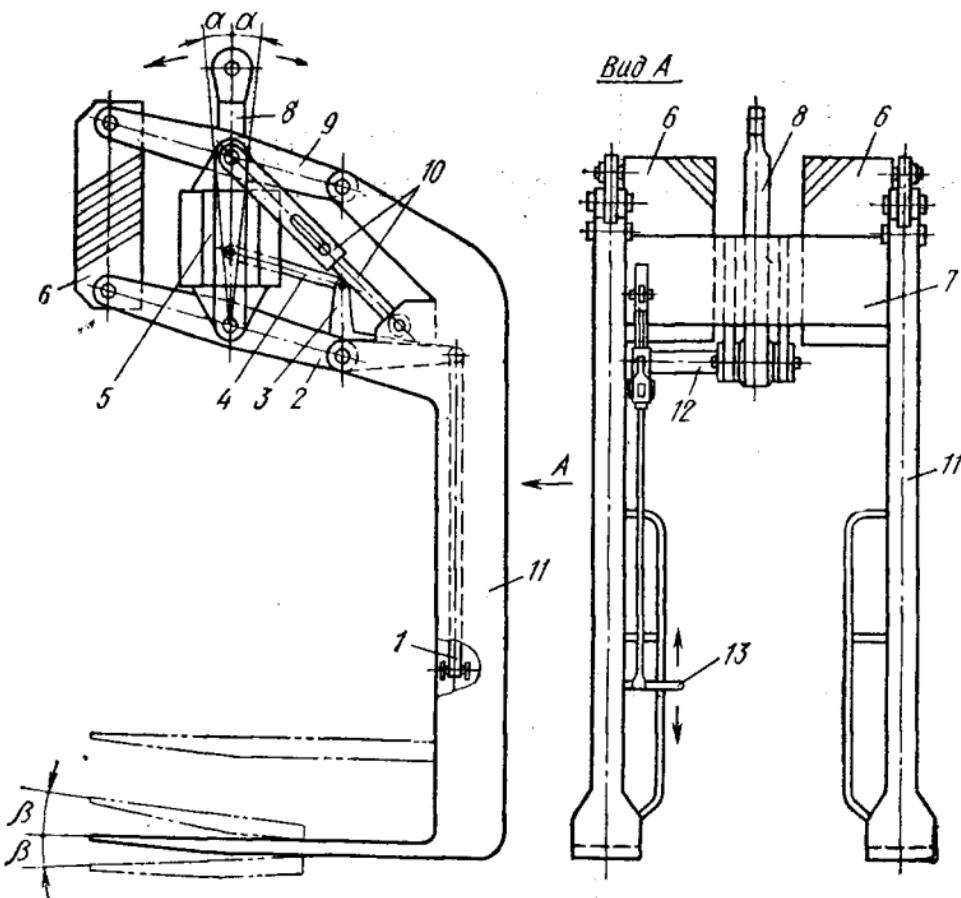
Грузозахватные устройства с горизонтальными поворотными лапами для перегрузки штучных грузов:
